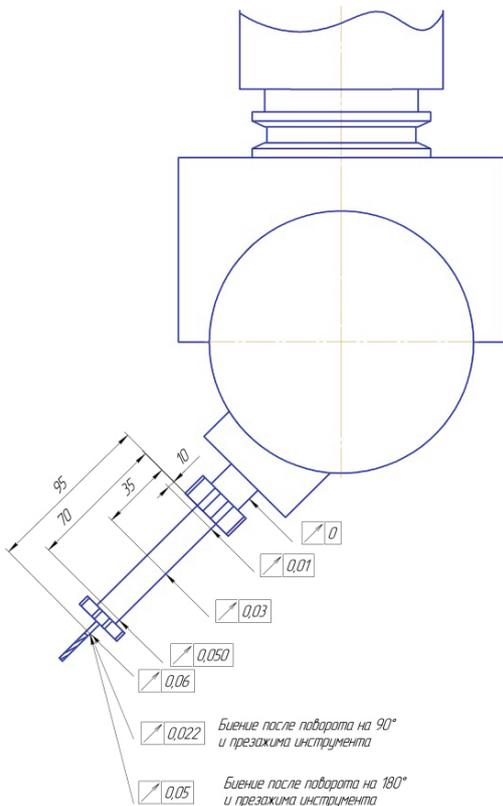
Схема измерения биения удлинительной оправки и фрезы, установленной в угловой головке для обработки радиусных канавок пресс-форм РТИ
